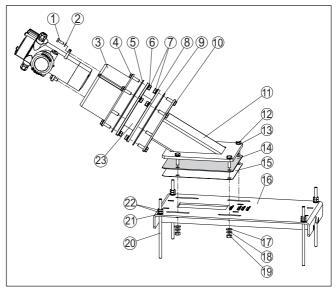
Dispositivo di fissaggio, lato sensore (MINITRAC)
